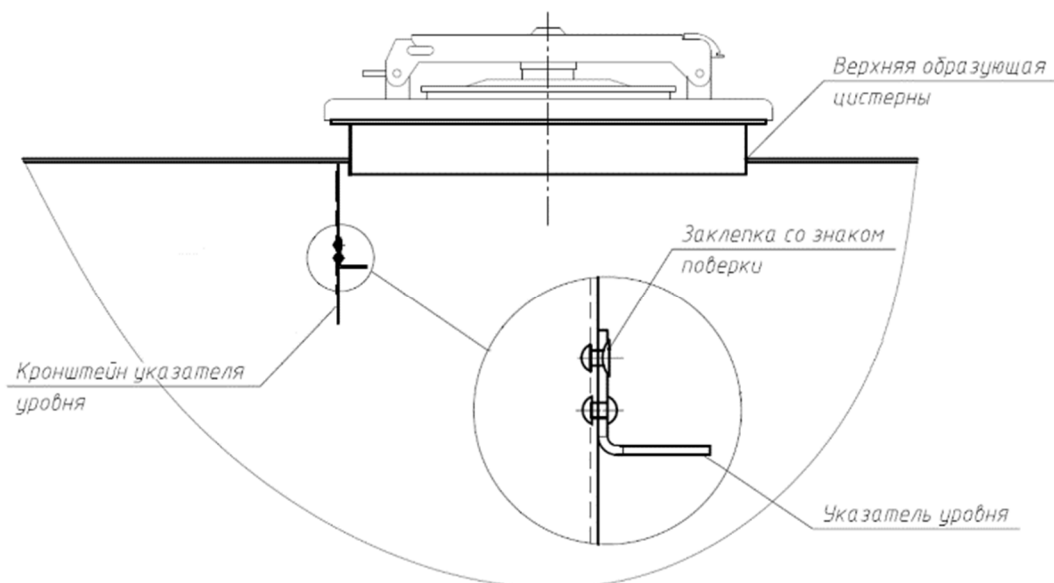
Схема пломбировки от несанкционированного изменения положения указателя уровня налива, обозначение места нанесения знака поверки
